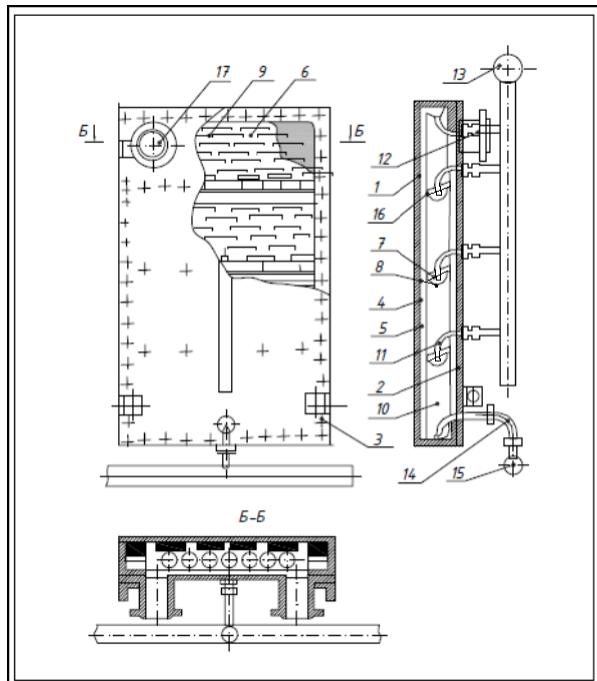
Конструктивная разработка кессона с капиллярно-пористой системой охлаждения кессона с пластинами жесткости: 1 – корпус; 2 – крышка; 3 – болт; 4 – стенка; 5 – капиллярно-пористая структура; 6 – пластина; 7 – артерия; 8 – корытце; 9 – отверстие; 10 – канал; 11, 17 – патрубок; 12 – труба; 13, 15 – коллектор; 14 – сифон; 16 – пластины жесткости
